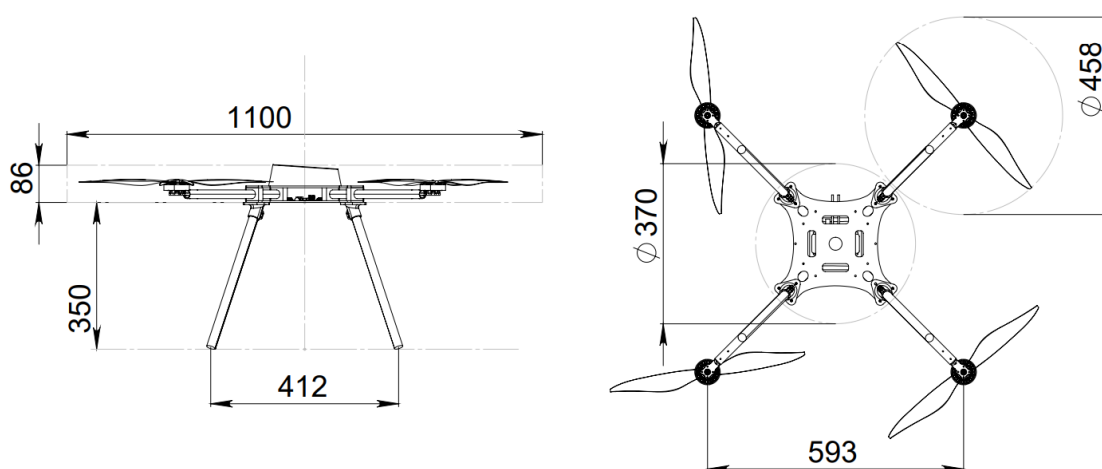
Размеры БВС для установки устройства захвата сейсмодатчика
